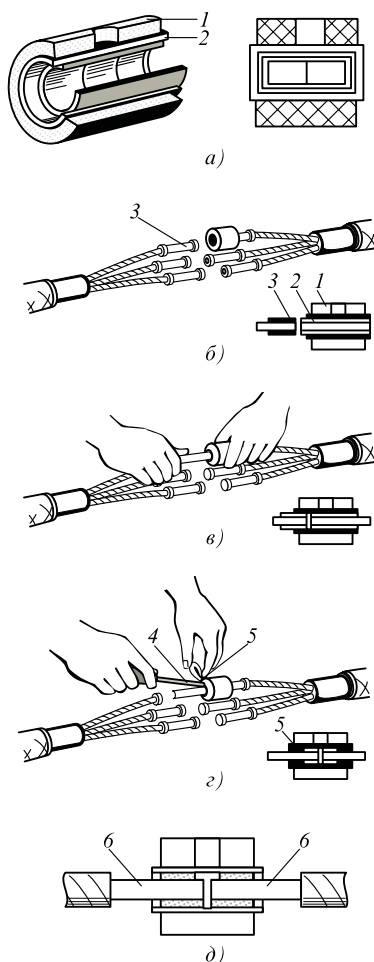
Процесс подготовки алюминиевых жил кабеля к сварке в термитном патроне:
